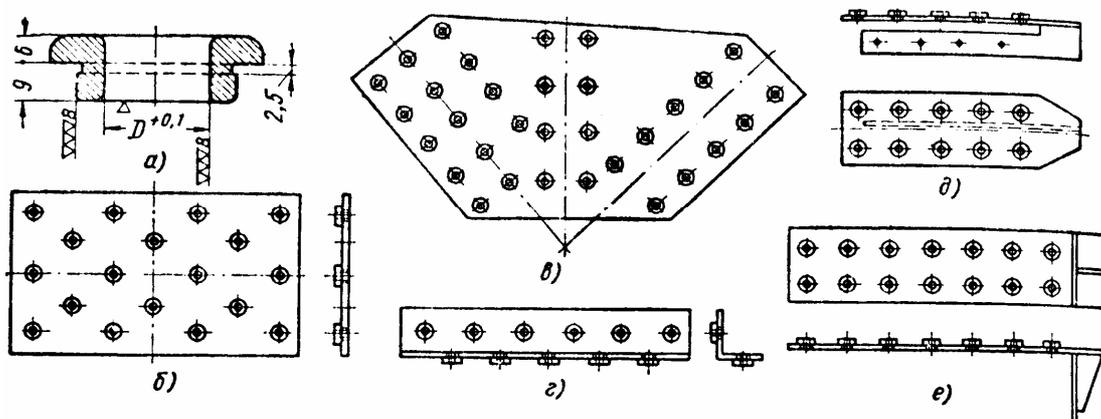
Кондуктора для сверления монтажных отверстий в стыках:
